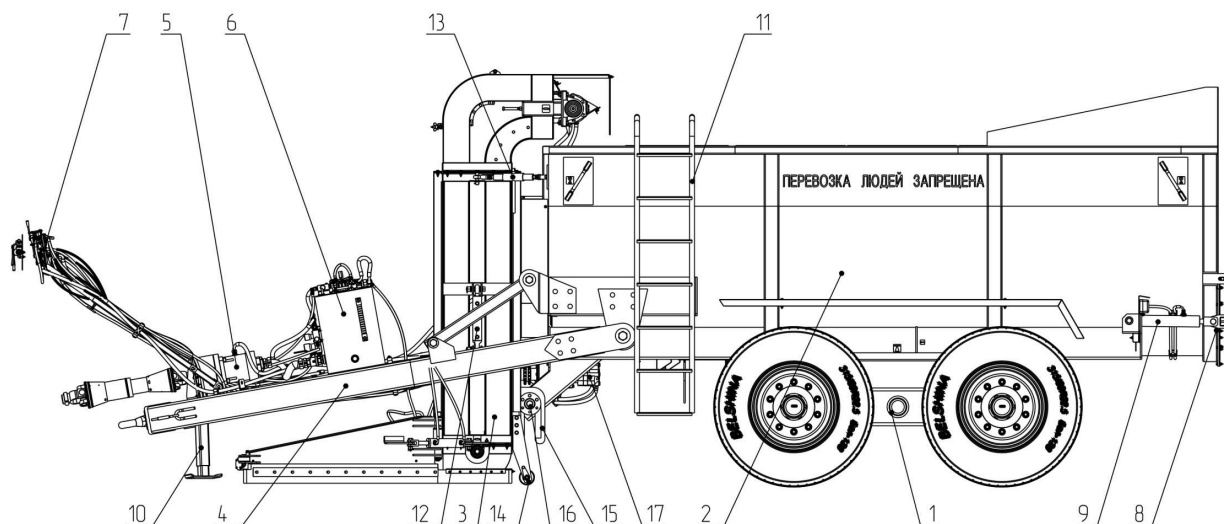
Технологическая схема агрегата: 1 – шасси; 2 – кузов; 3 – скрепер-элеватор; 4 – сница; 5 – гидронасос; 6 – масляный бак; 7 – пульт управления; 8 – борт задний; 9 – гидроцилиндры закрытия-открытия борта заднего; 10 – опора; 11 – лестница; 12 – гидроцилиндр подъема элеватора; 13 – талрепы; 14 – опоры катковые; 15 – кронштейн; 16 – ось; 17 – гидромотор привода шнека выгрузного
